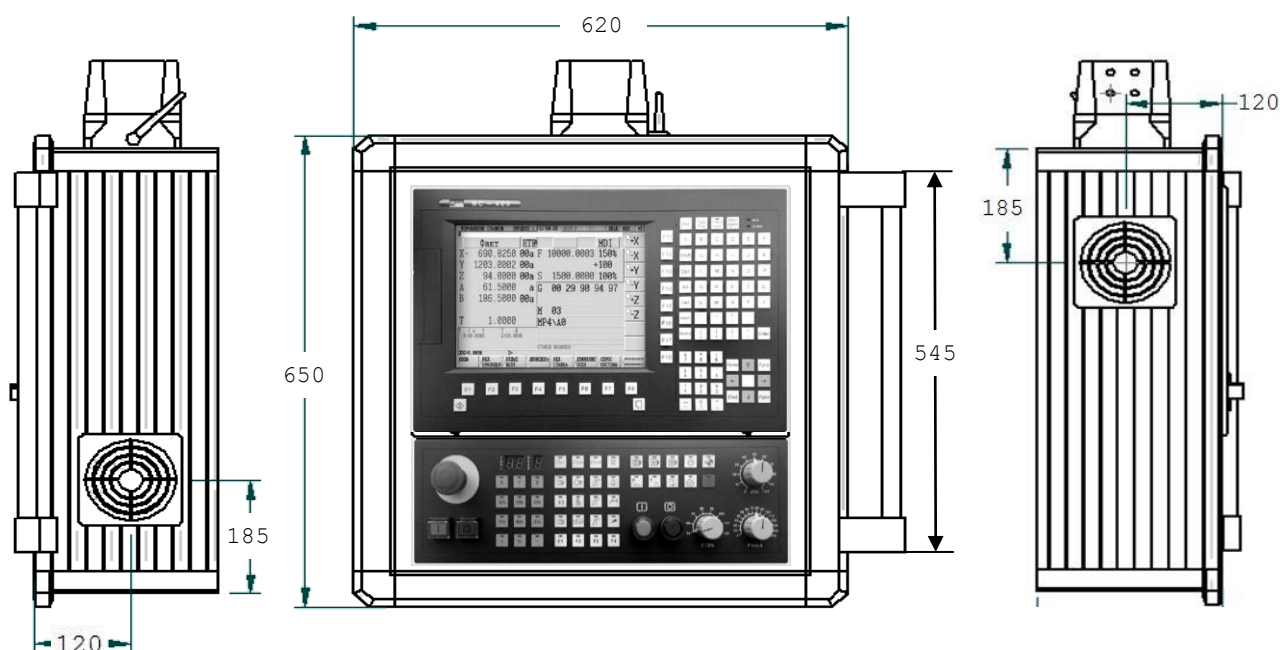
Габаритные размеры кожуха для УЧПУ NC-400.
